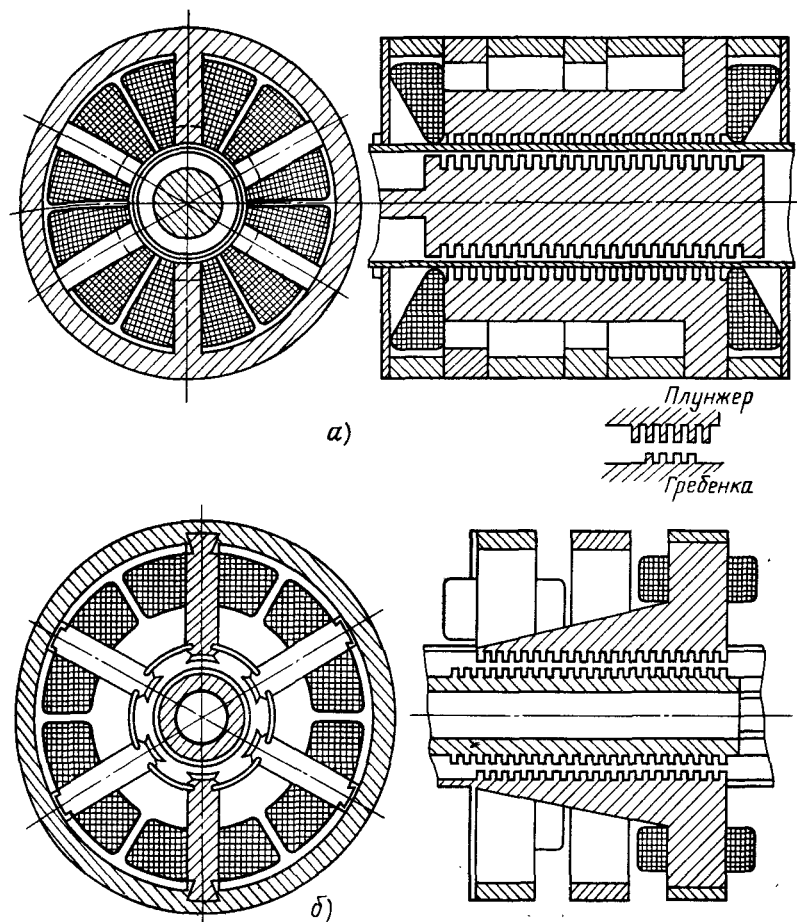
Линейный цилиндрический гребенчатый электродвигатель
